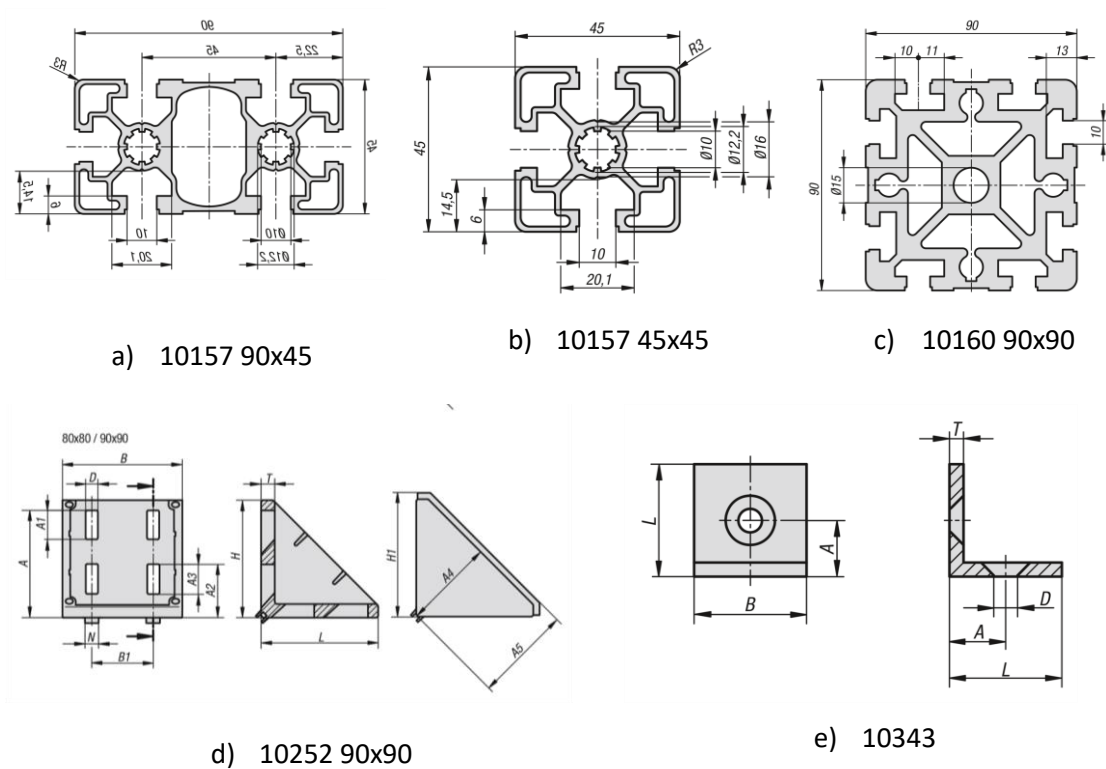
a) perfil utilizado nas travessas do sistema de corte; b) perfil utilizado nos reforços do armário; c) perfil utilizado na base da estrutura; d) cantoneiras utilizadas na base; e) cantoneiras utilizadas na estrutura.
